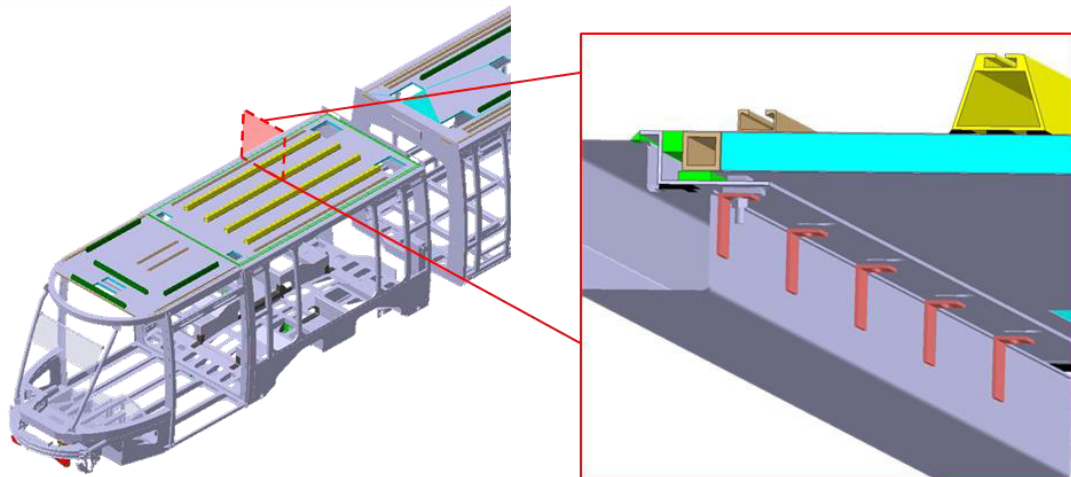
Beispiel einer konventionellen Dachstruktur einer Niederflurstraßenbahn [1]
